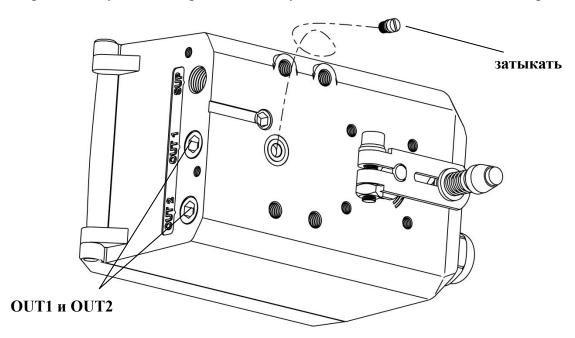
Принципиальная схема вилки и воздуховыпускного отверстия.
